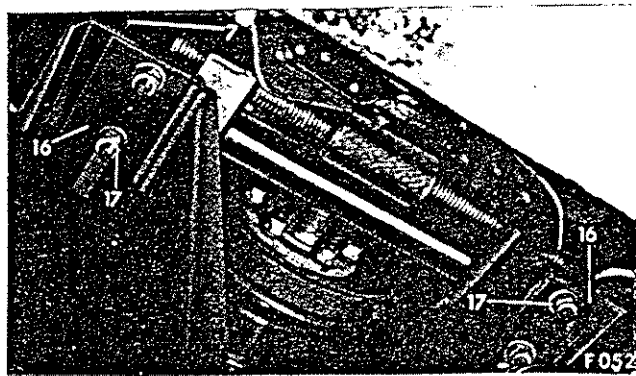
Angesetztes Spreizwerkzeug zum Zusammenpressen der Zahnstangengummis
